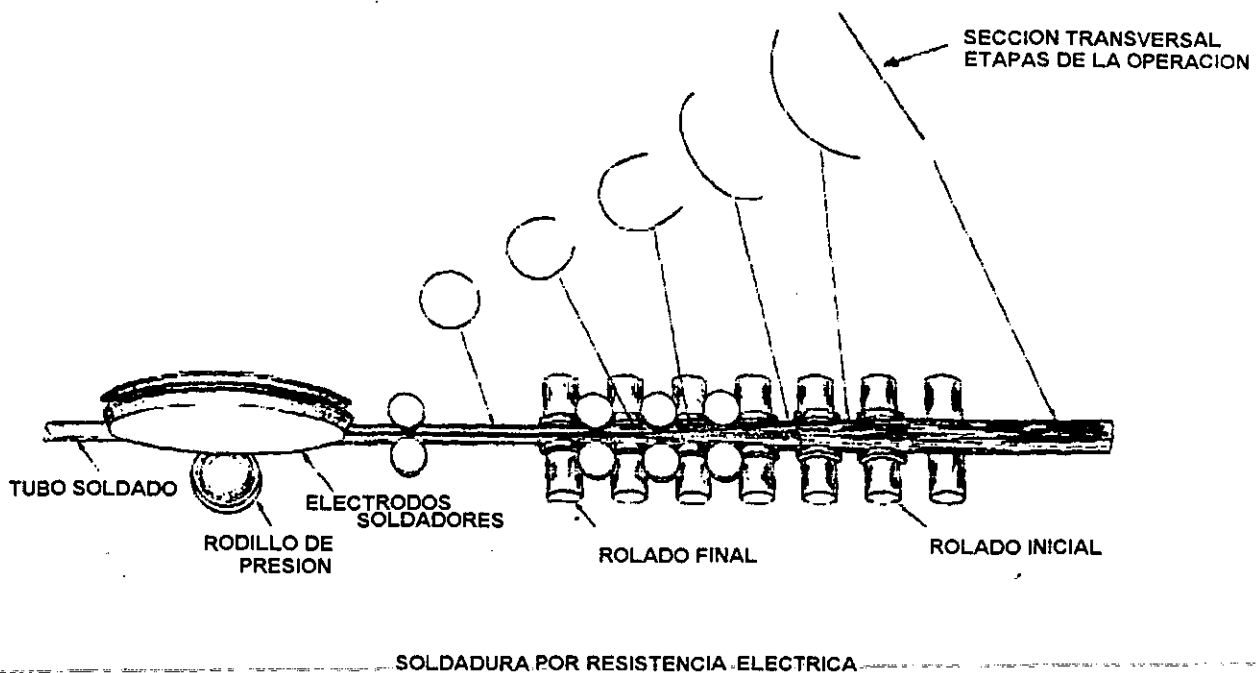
Proceso de soldadura por resistencia eléctrica para producir tubos.
